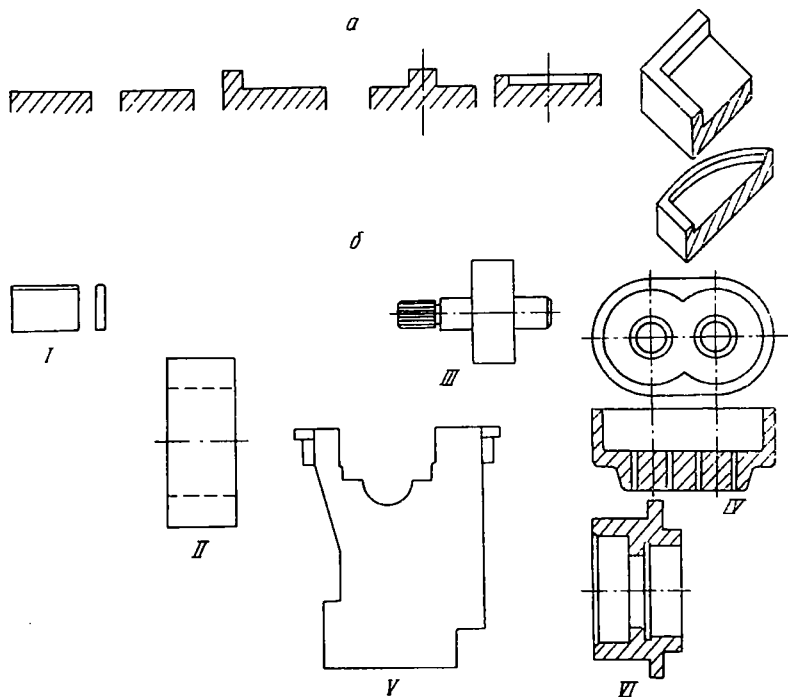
Плоские поверхности: *a* — схемы обрабатываемых поверхностей; *б* — примеры поверхностей на деталях. *I* — лопатка насоса; *II* — статор лопастного насоса; *III* — шестерня масляного насоса; *IV* — корпус масляного насоса; *V* — блок цилиндров; *VI* — ступица реакторов
